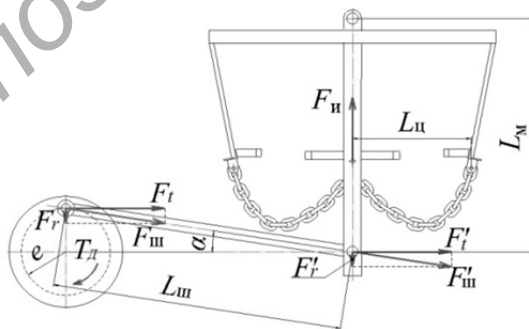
Среднее положение механизма цепного агрегата с волновой рабочей камерой
